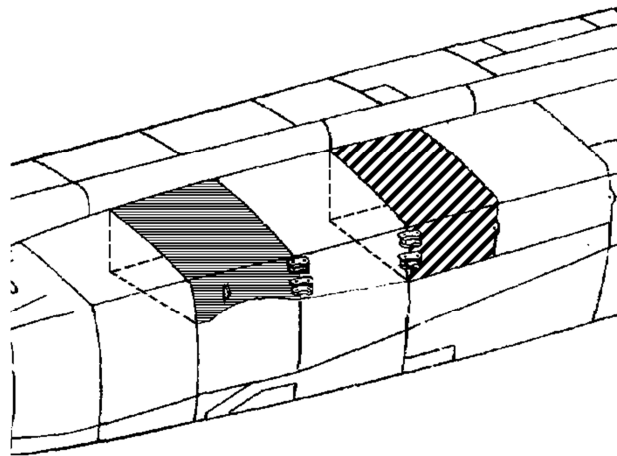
Выделенные штриховкой зоны - типовые сварные отсеки фюзеляжа сверхзвукового самолета
